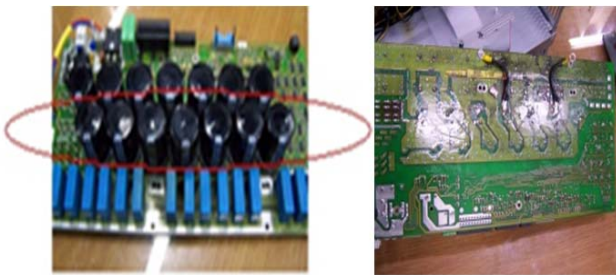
전해 커패시터의 고장 및 PCB 사고 모습
